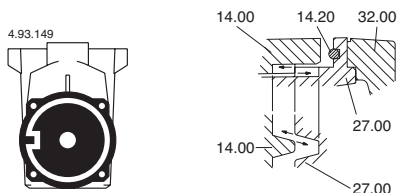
Ориентиры для сборки корпуса насоса (14.00) – крышки диффузора (27.00)
